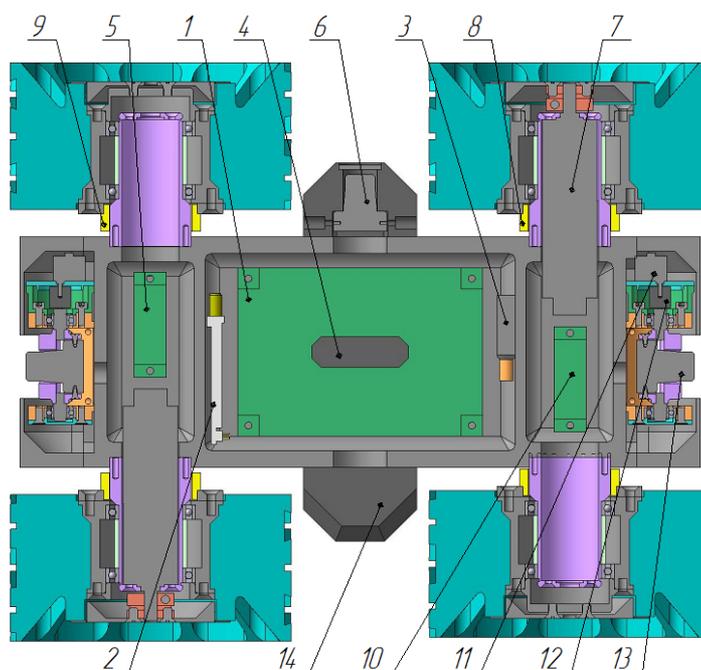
Продольный разрез корпуса разрабатываемого робота: 1 – основная плата управления; 2 – плата передачи сигналов управления; 3 – плата передачи видеосигнала; 4 – гироскопический датчик; 5 – плата управления двигателем узла качания передней камеры; 6 – боковая камера; 7 – мотор-редуктор Faulhaber 2642 26A; 8 – шкив ременной передачи ведущего колеса; 9 – шкив ременной передачи ведомого колеса; 10 – плата управления двигателем узла качания задней камеры; 11 – мотор-редуктор Faulhaber 1512; 12 – соединительная муфта узла качания камеры; 13 – поворотная камера; 14 – кожух боковой камеры
